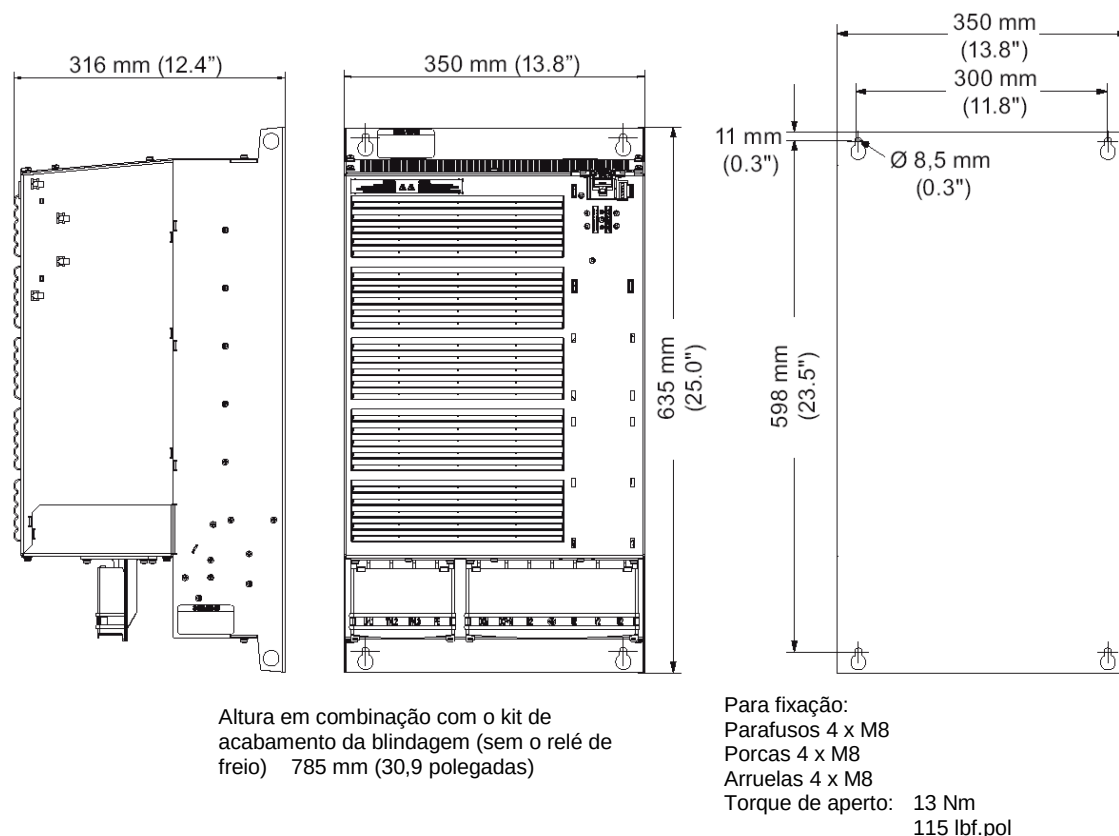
Dimensões e padrão de perfuração, FSF não filtrado (HO 45 kW ... 75 kW)
